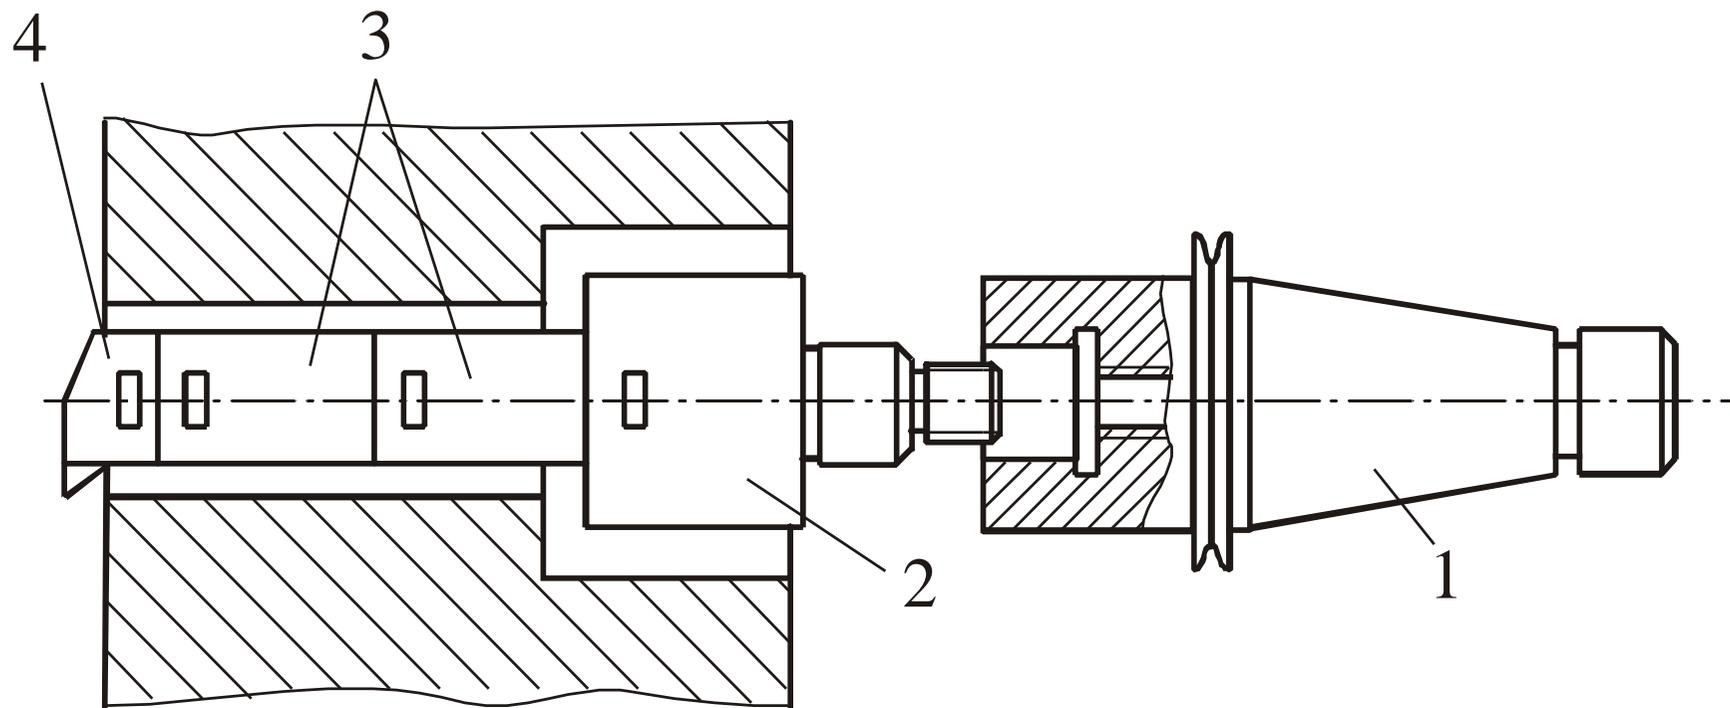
Инструментальный расточной блок из стандартных модулей:
